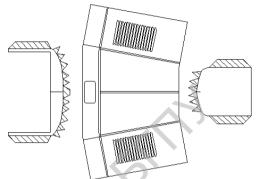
Пример - развертка капота ЗИС-8 [6]
